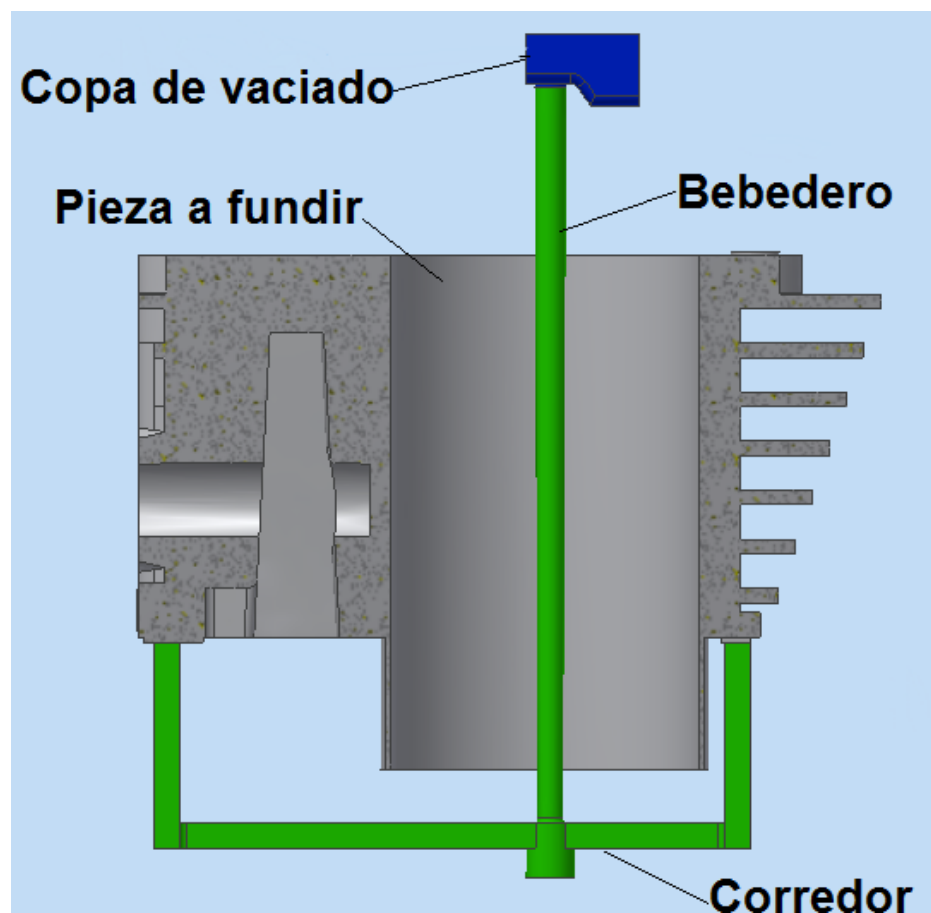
Vista seccionada del sistema de llenado para la fundición del bloque
